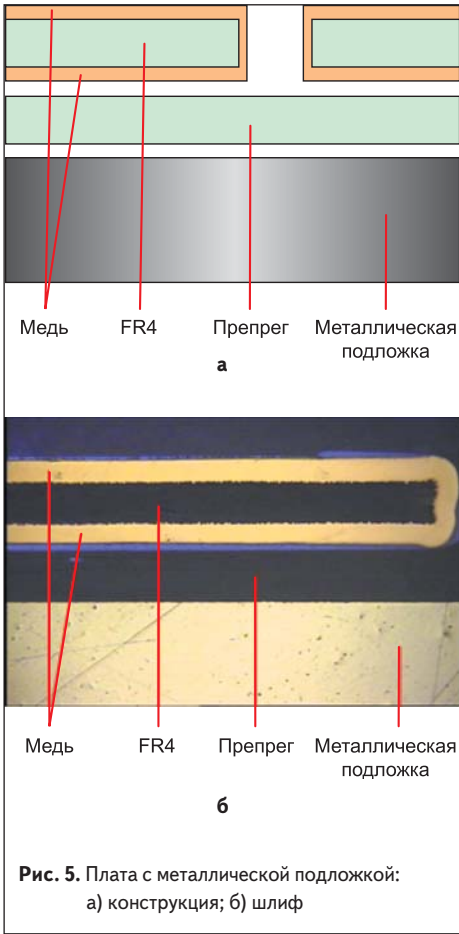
Плата с металлической подложкой: а) конструкция; б) шлиф
